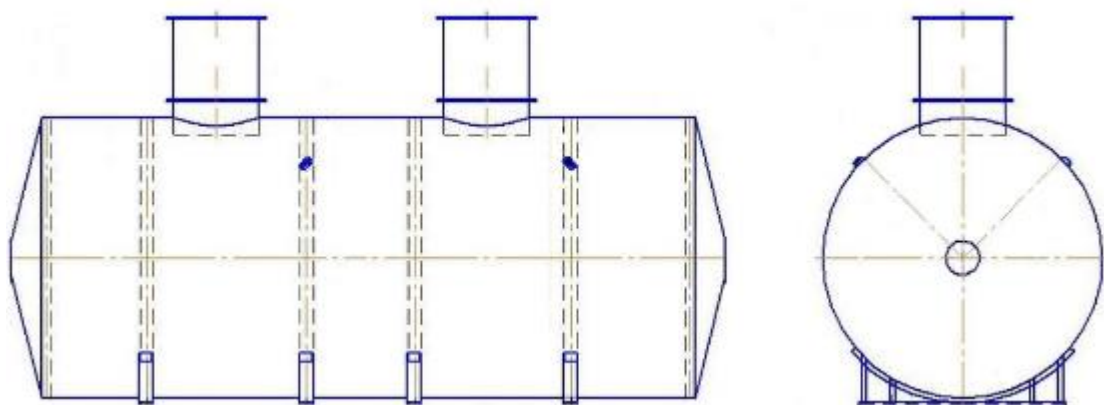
Эскиз общего вида резервуара РГС-50
